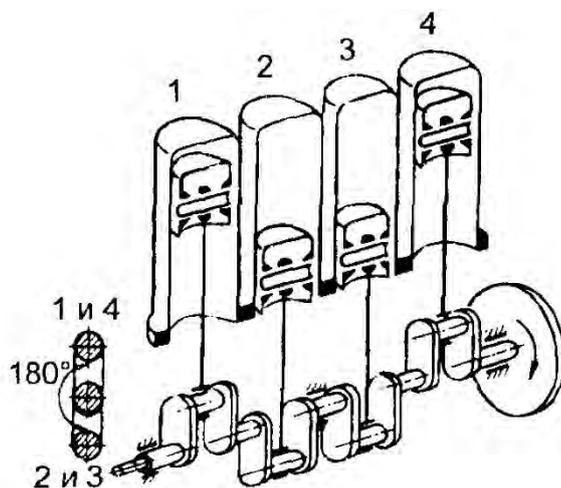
Коленчатый вал рядного четырехцилиндрового двигателя
